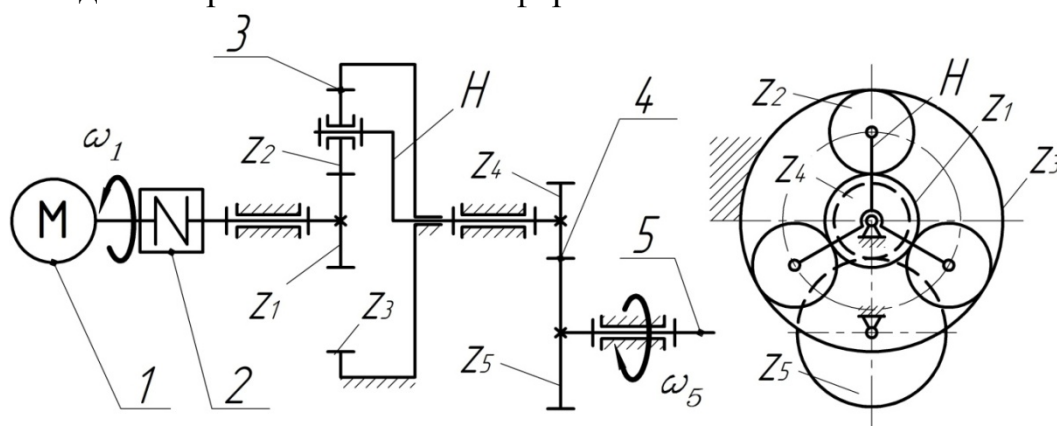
Кинематическая схема привода с планетарным механизмом
